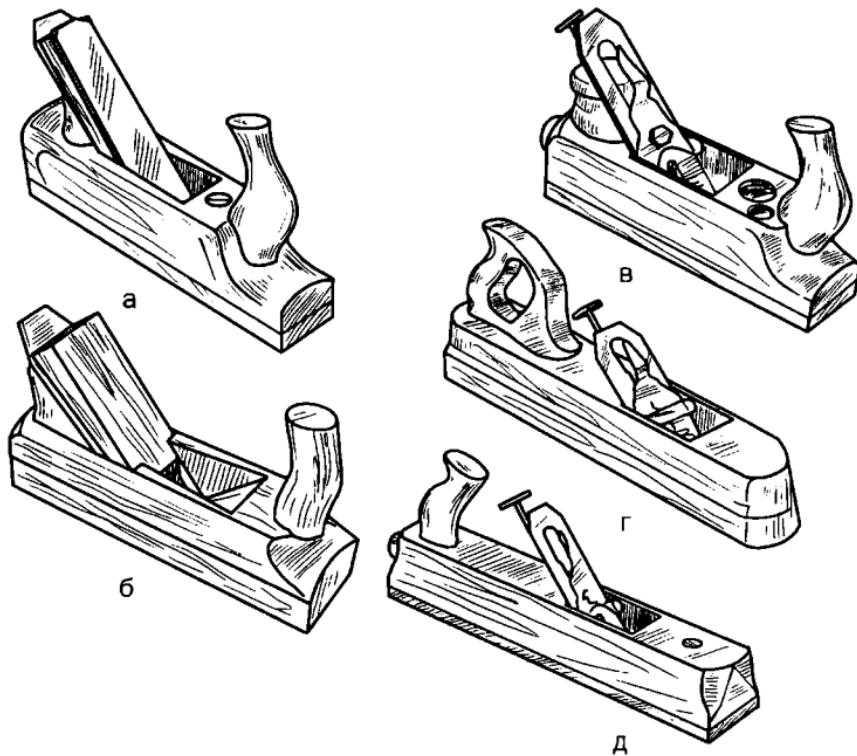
Некоторые строгальные инструменты: а — шерхебель; б — рубанок; в — шлифтник; г — фуганок; д — полуфуганок
